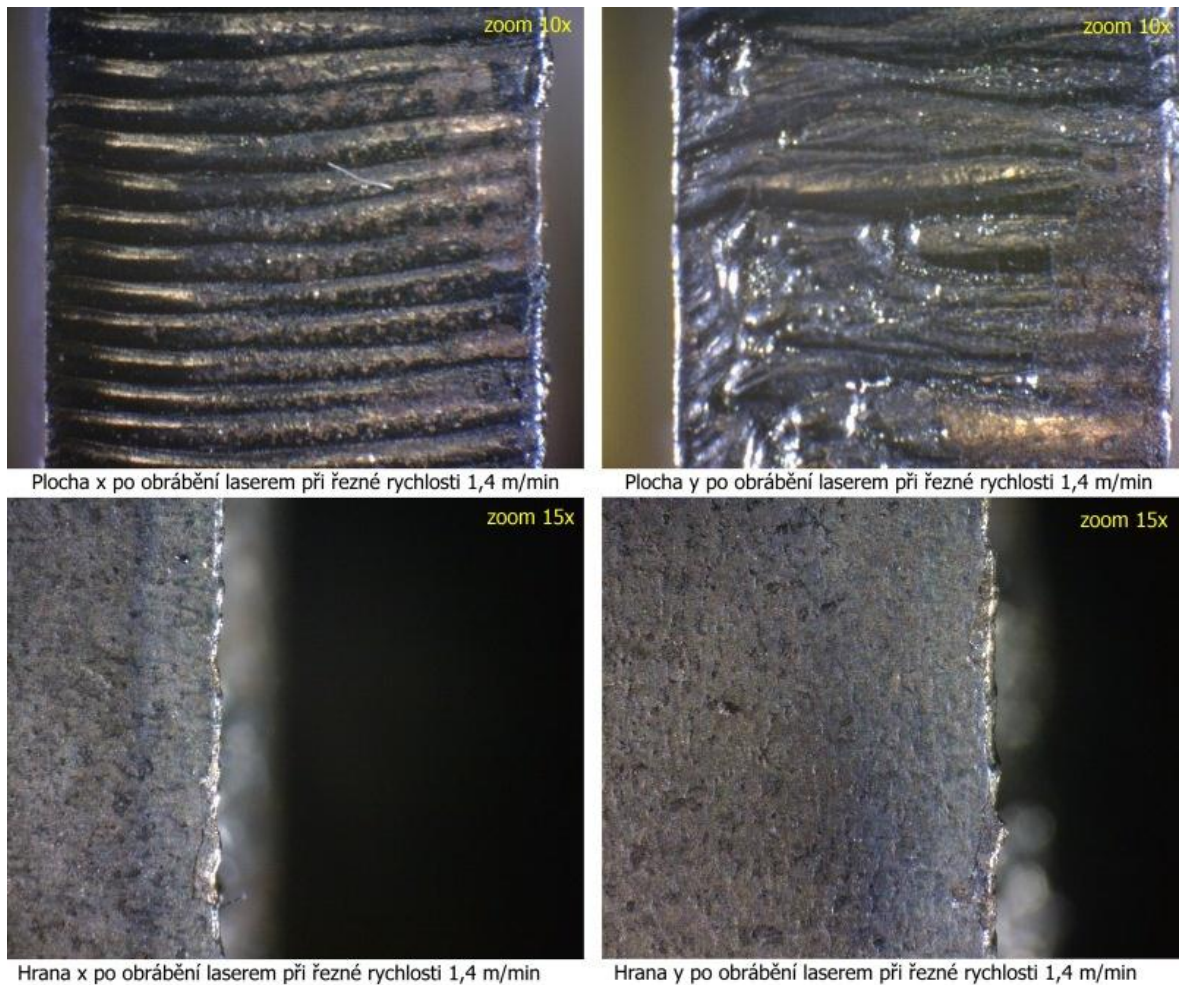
Snímky z mikroskopu vzorku 5 obráběného laserem - materiál 11 375
